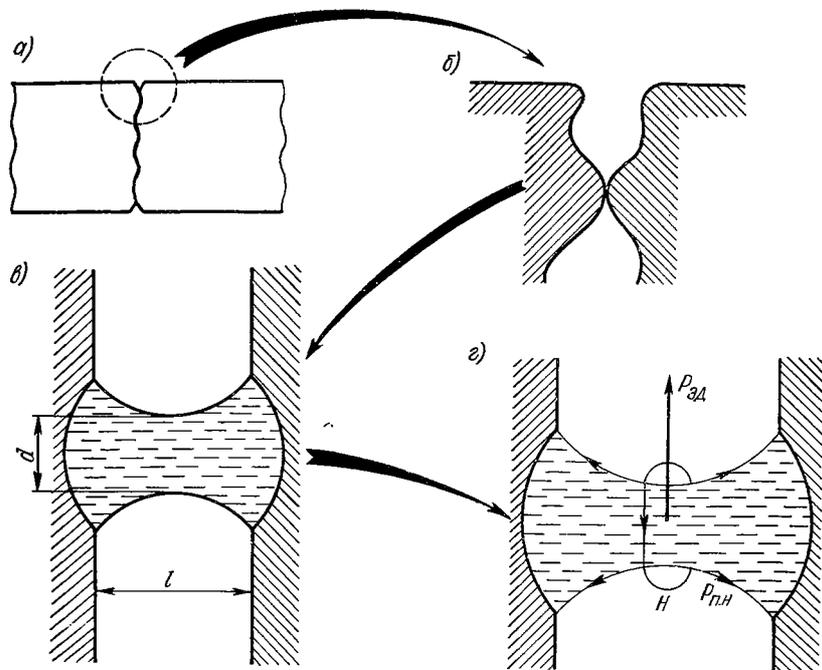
Схема образования и последующего взрыва единичного контакта при стыковой сварке оплавлением
